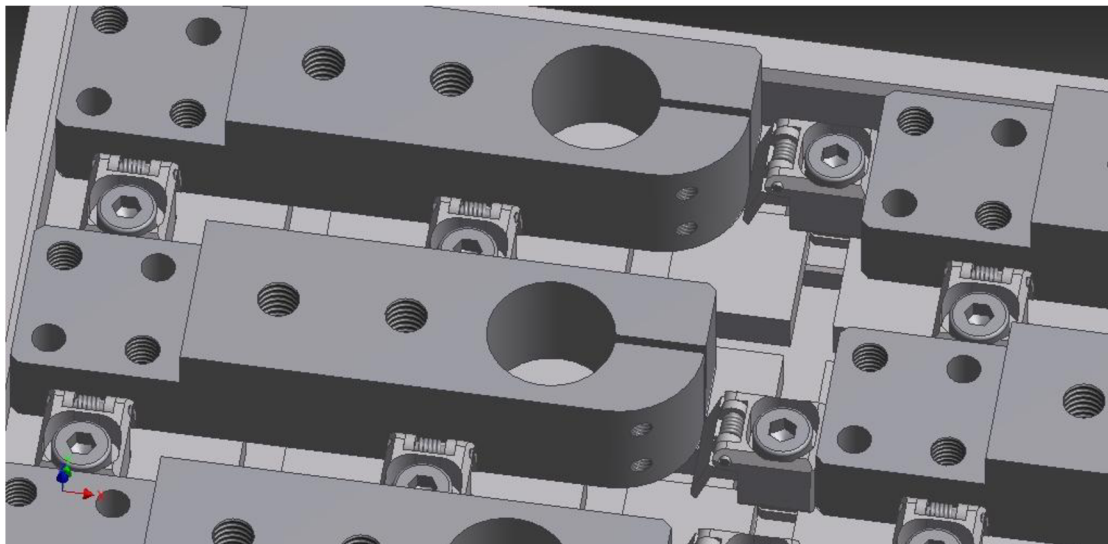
Paleta s upnutým jedním obrobkem. [vlastní zpracování]
